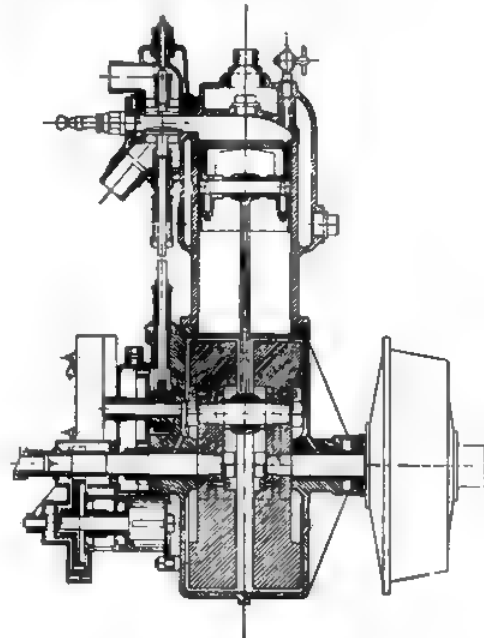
Schnitt durch 1 cyl. Motor u. Pumpe.
